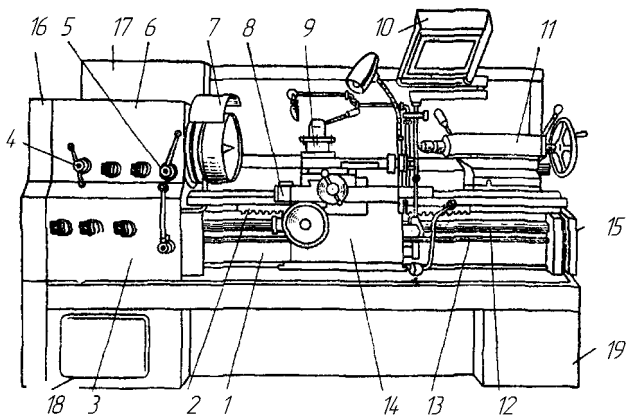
Общий вид токарно-винторезного станка 16K20
